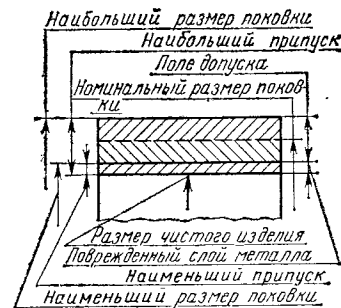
Схема расположения припусков и допусков на поковке
